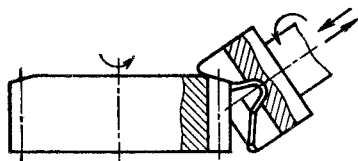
Схема обработки торцовых поверхностей зубьев пустотелой конусной торцовой фрезой
